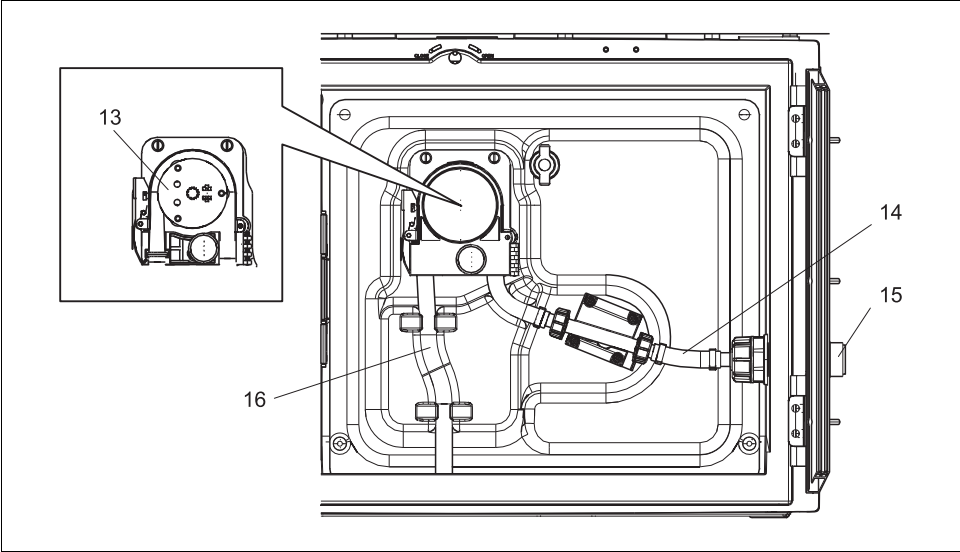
Ersatzteile für Ausführung mit Schlauchpumpe
